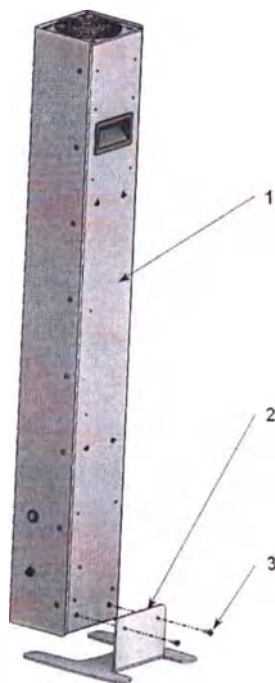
Монтаж облучателя РП-80 на опорную стойку. 1- Облучатель; 2- Опорная стойка; 3- Винт М5
